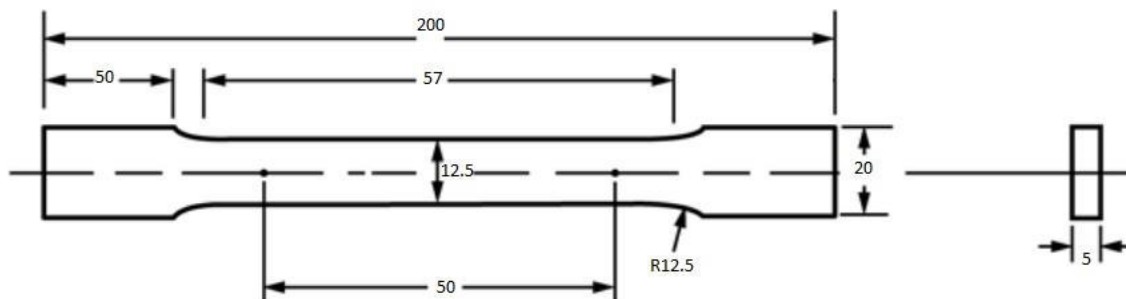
Dimensiones de la probeta de material base (Fuente propia)
